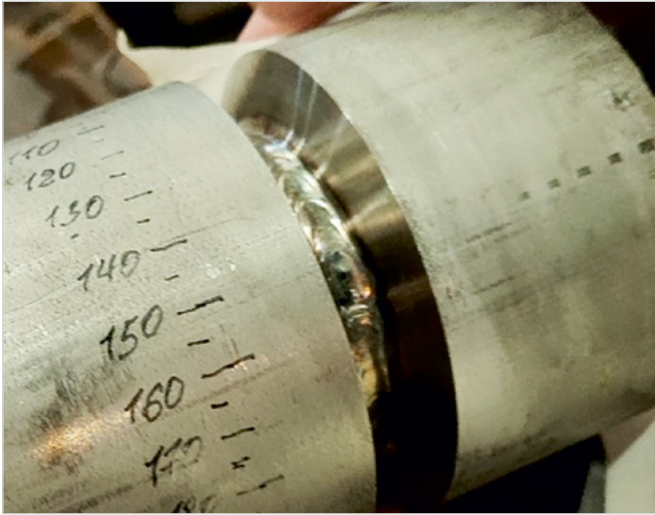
Разметка с шагом 5 мм по периметру сварного соединения
